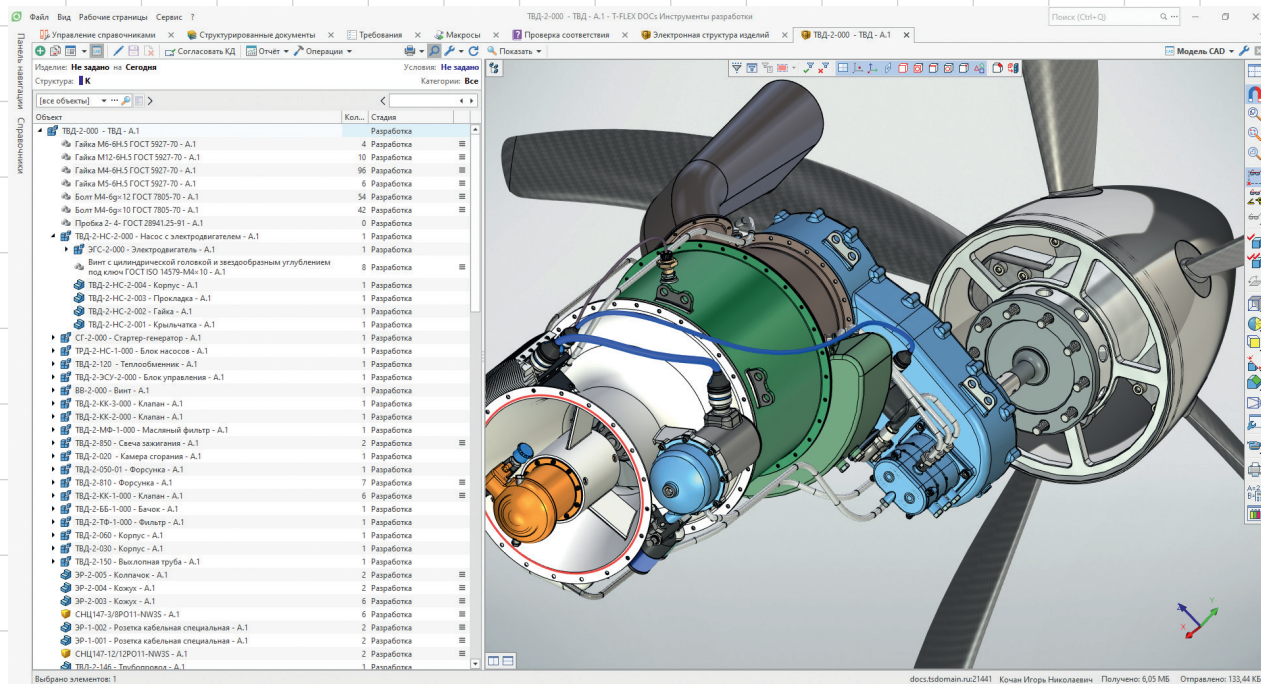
Пример сборочной единицы — двигательная установка с винтом для БПЛА
